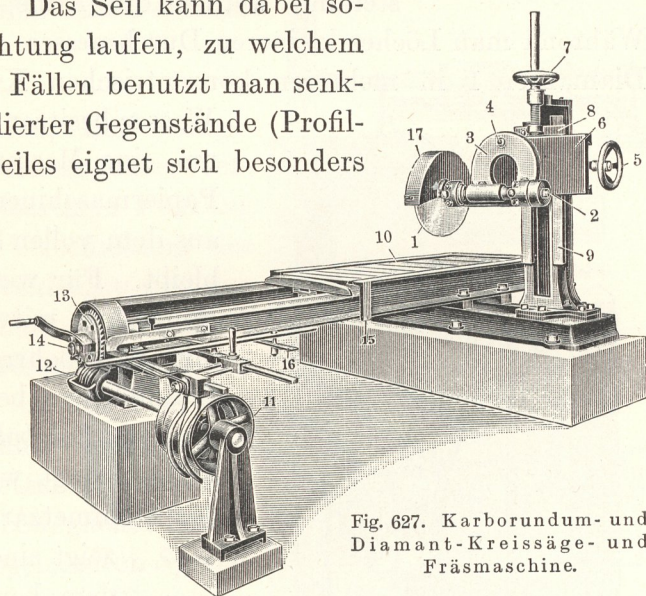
Karborundum- und Diamant-Kreissäge- und Fräsmaschine.
